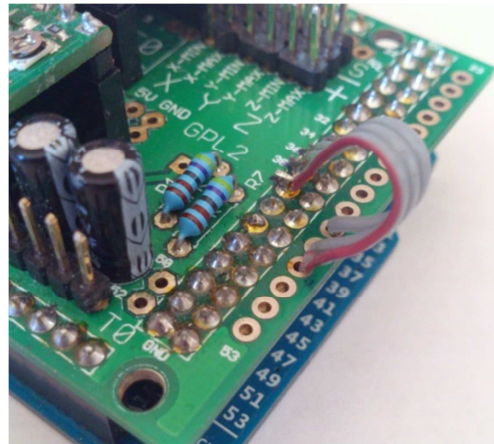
Soldadura sobre la placa *Ramps
